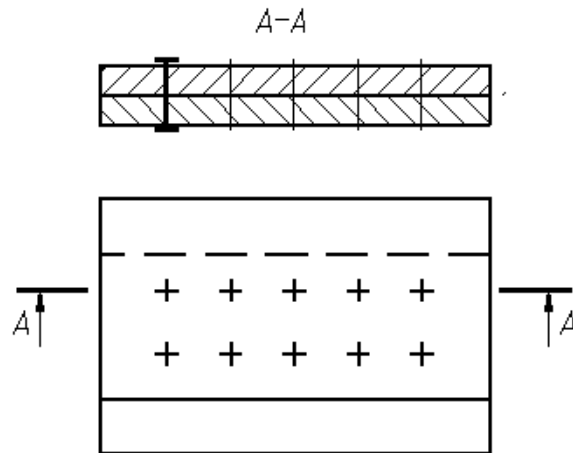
Изображение на сборочном чертеже соединения с одинаковыми заклепками
